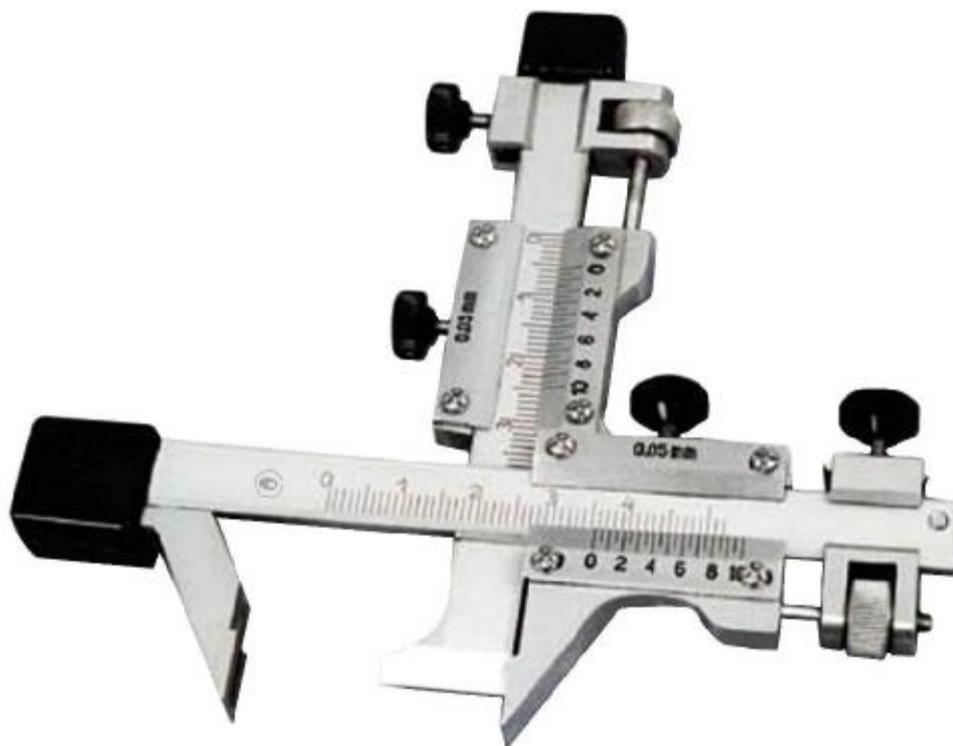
Общий вид штангензубомера с нониусами ШЗН
